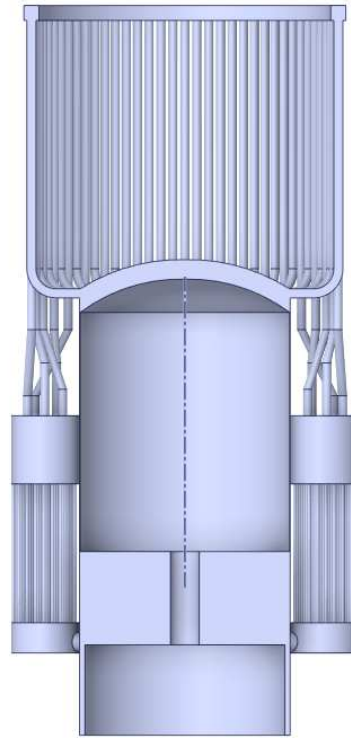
Desenho esquemático do motor Stirling GPU-3.
